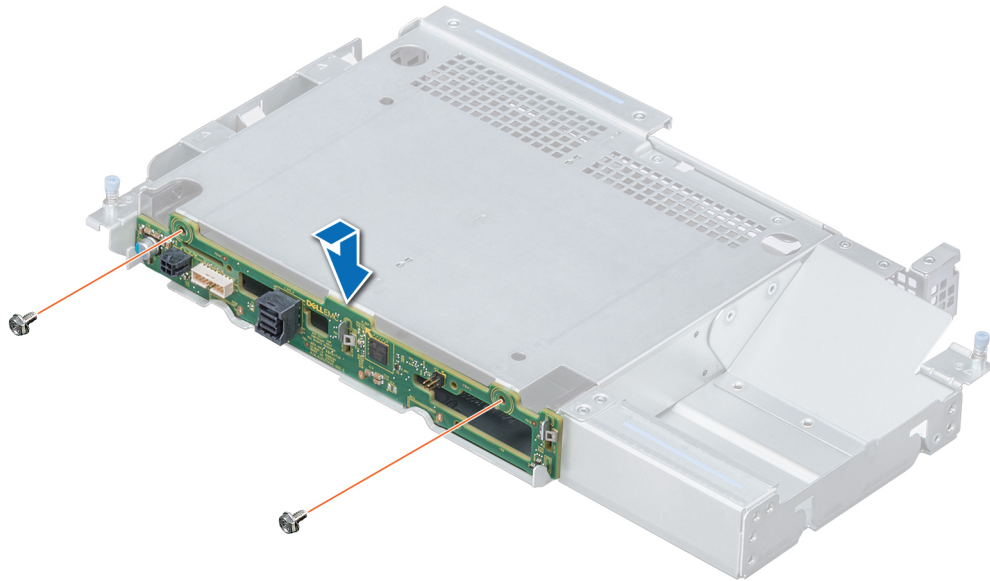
Installation du fond de panier de disques de 3,5 pouces arrière
